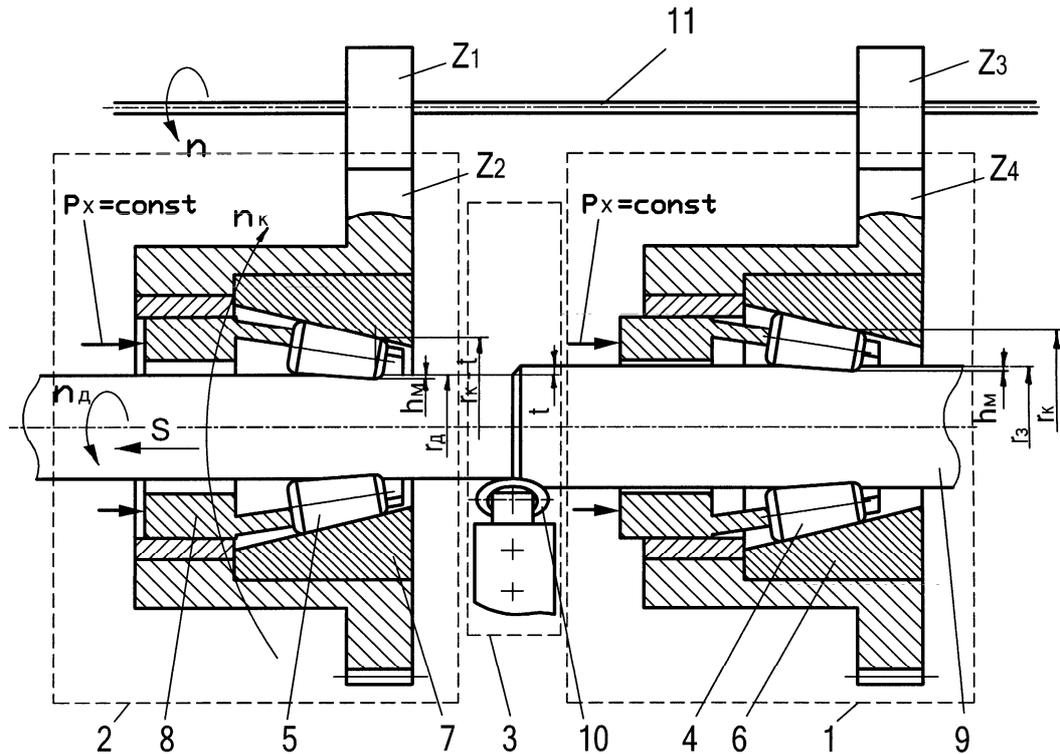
Схема работы комбинированного инструмента: 1 – вспомогательный обкатник; 2 – основной обкатник; 3 – резцовая головка; 4, 5 – деформирующие ролики; 6, 7 – опорные конусы; 8 – сепаратор; 9 – обрабатываемая заготовка; 10 – резец резцовой головки; 11 – трансмиссионный вал; $z_1 \dots z_4$ – зубчатые колеса.
